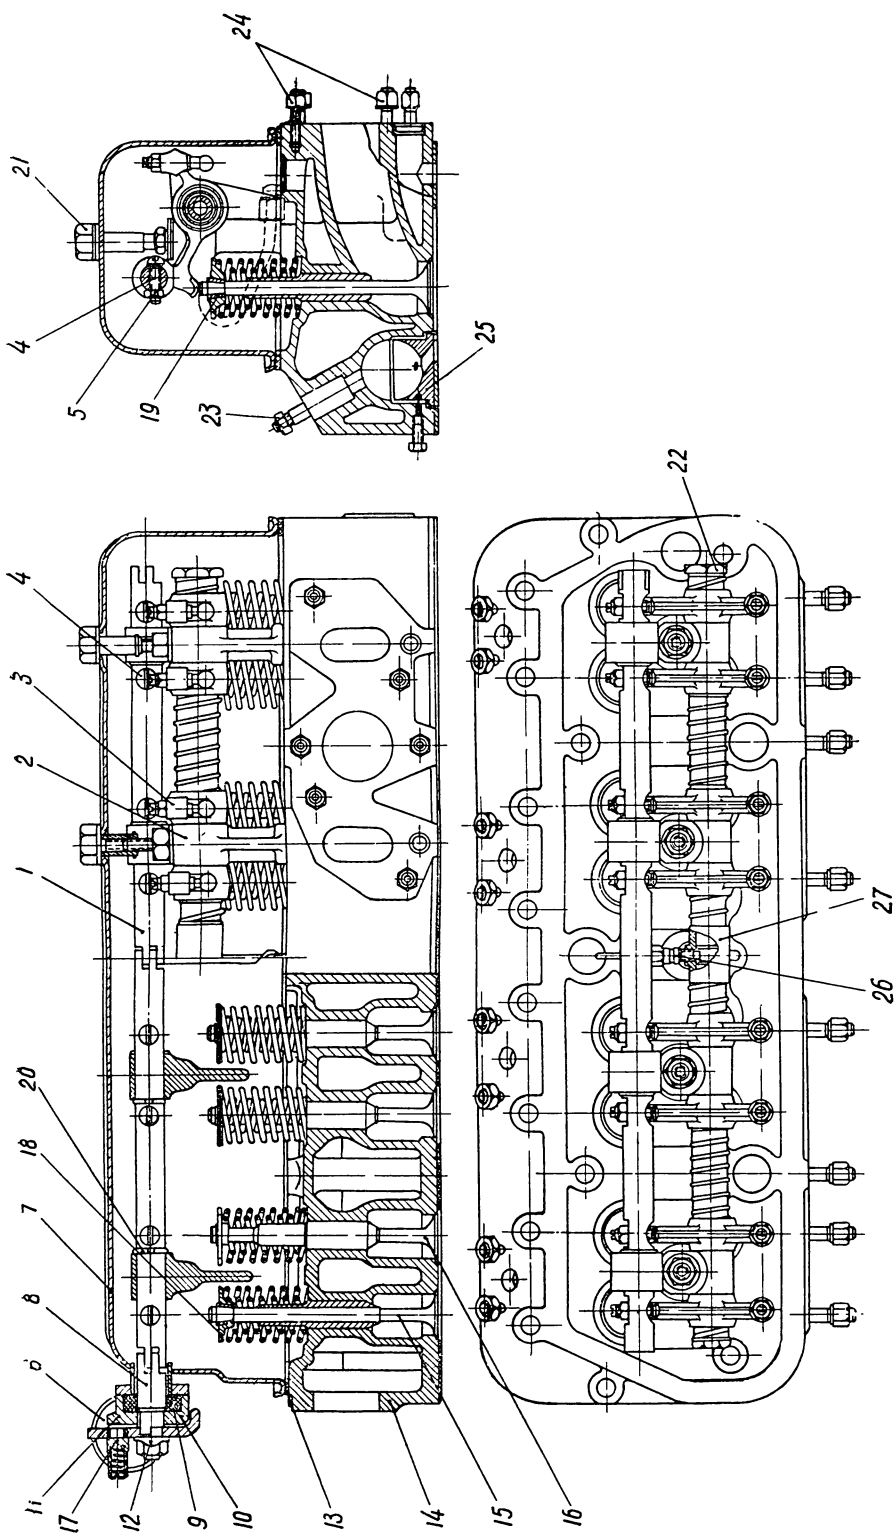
Головка блока цилиндров в сборе с клапанным механизмом и механизмом Декompрессии:
